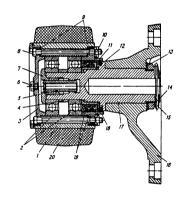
Поддерживающий каток: 1 – ступица; 2 – подшипники; 3 – крышка; 4 – втулка; 5 – стопорный палец; 6 – пробка; 7 – грибок; 8 – болт; 9 – прокладки; 10 и 14 – гайки;
